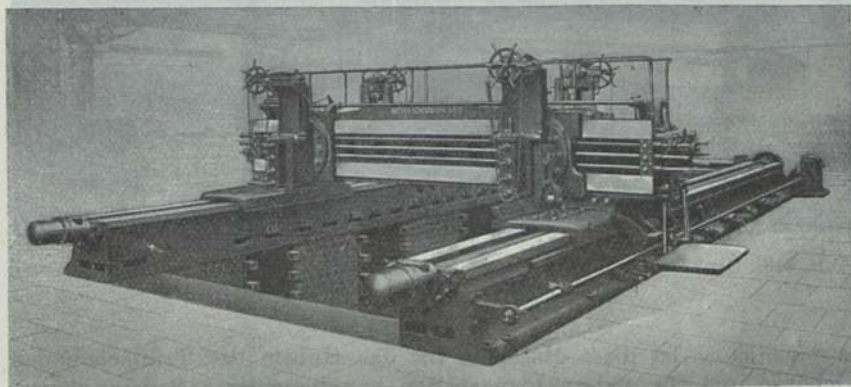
Neue Grubenhobelmaschinen der Kalker Maschinenfabrik, A.-G., Köln-Kalk.
